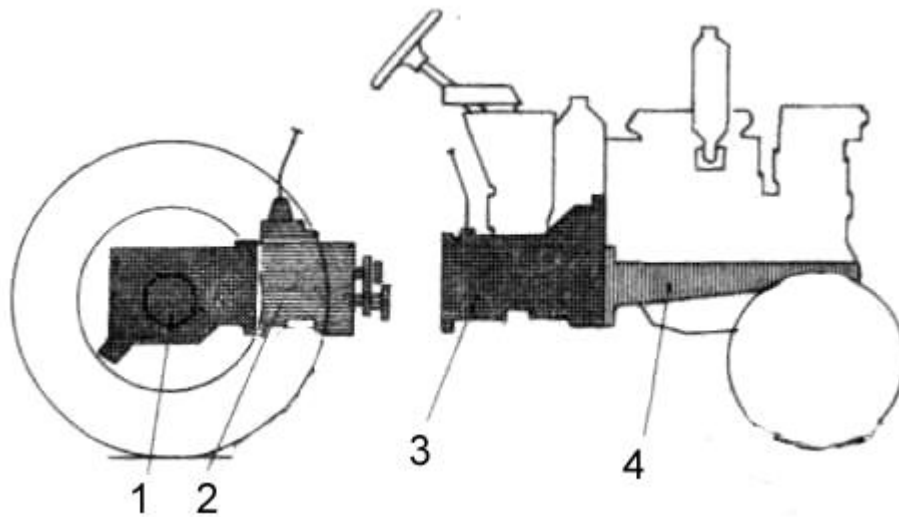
Схема від'єднання корпусу муфти зчеплення від коробки:
